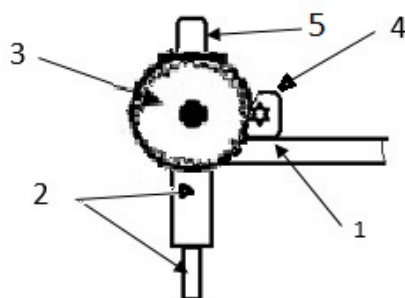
Схема узла преобразования вращательного движения вала в поступательное движение ноги: 1 – платформа; 2 – опорная нога; 3 – поворотная шестерня ноги; 4, 5 – шаговый двигатель
